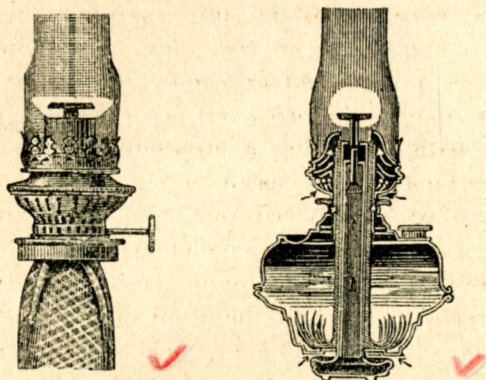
Круглий пальник: на ліво цілий, на право перекроєний на поздовж.
